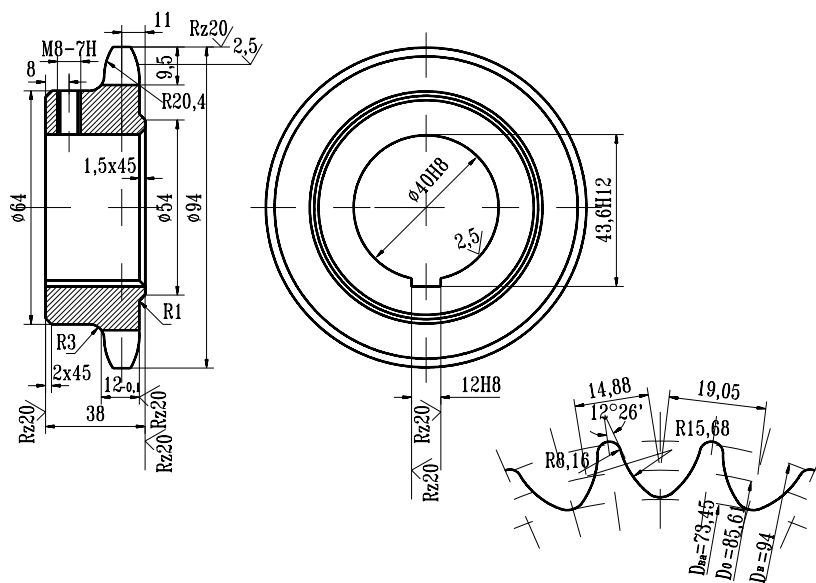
Звездочка автомата для разлива молока в бумажные пакеты
